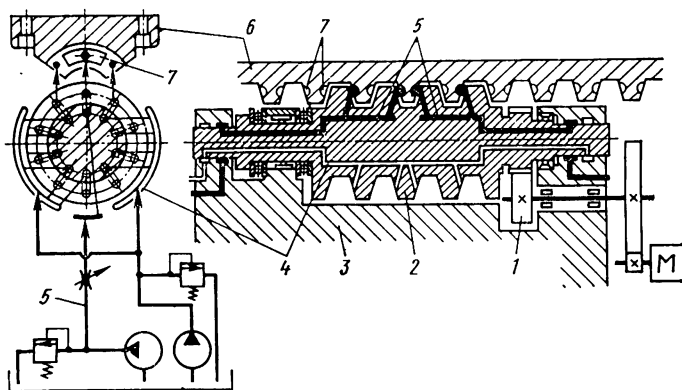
Схема червячно-реечной передачи механизма горизонтальной подачи суппорта с гидростатической смазкой
